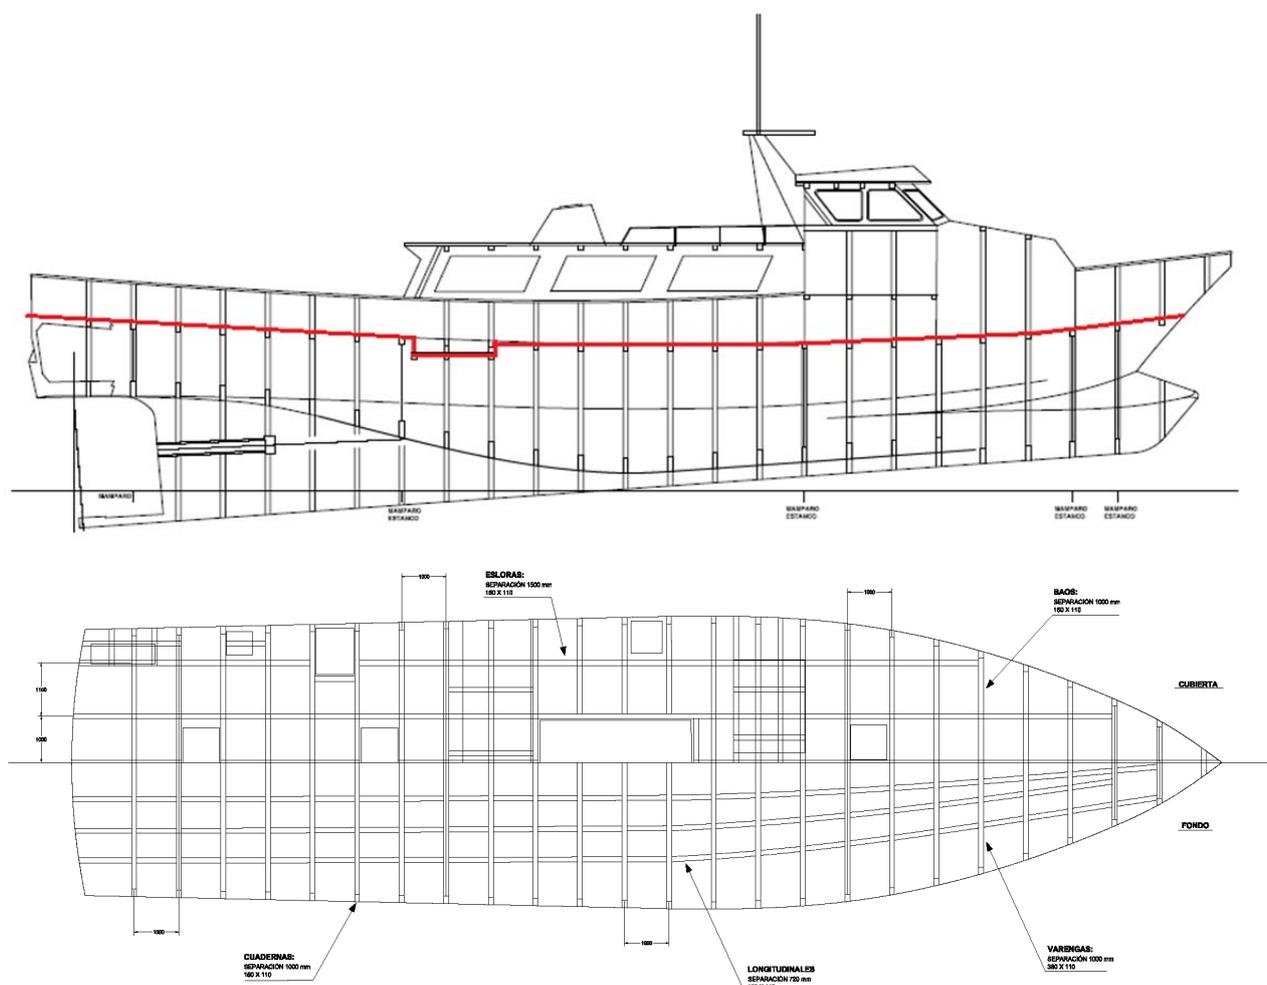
Plano estructural de la embarcación, en rojo destacada la cubierta principal.
